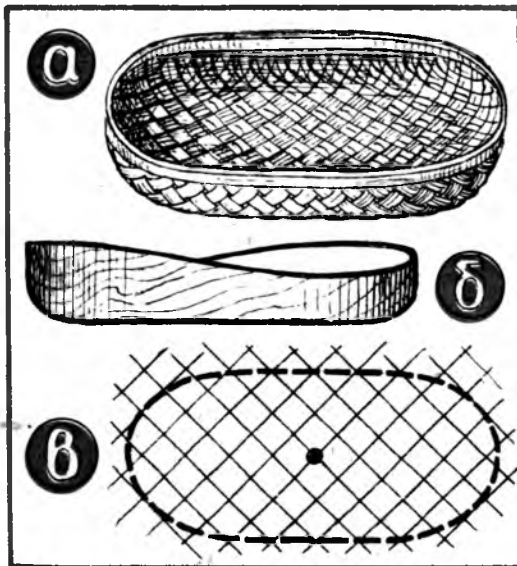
Овальная хлебница: а — хлебница; б — болванка-форма; в — разметка дна
